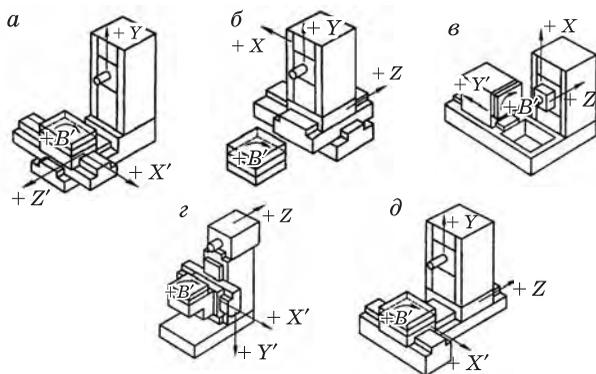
Примеры компоновок многоцелевых станков сверлильно-фрезерно-расточной группы с горизонтальным расположением шпинделя:
